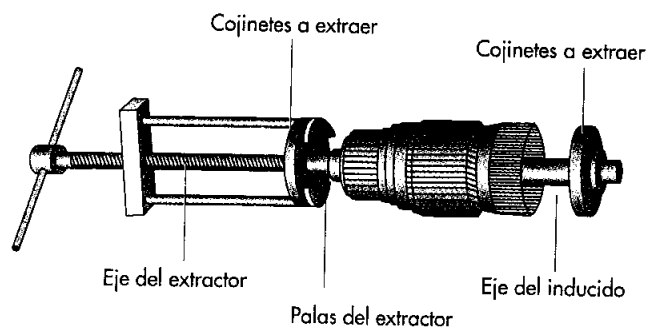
Extracción del cojinete del rotor de una máquina.
